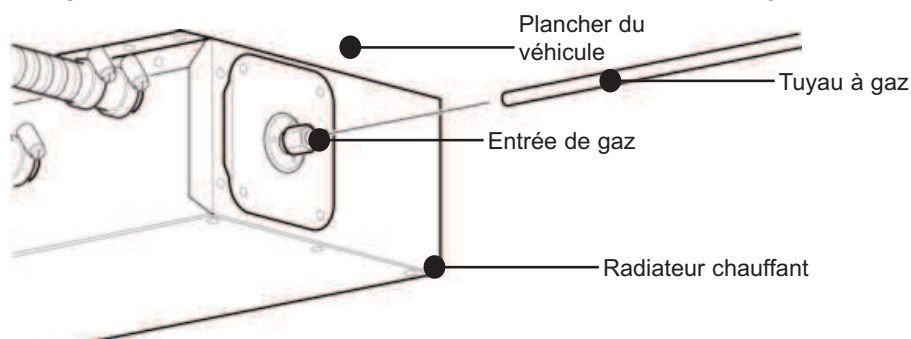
Installation sous plancher - Raccordement à l'alimentation de gaz
